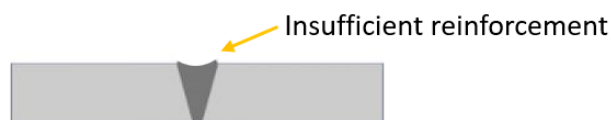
Armătură insuficientă prezentată prin desen 2-dimensional
